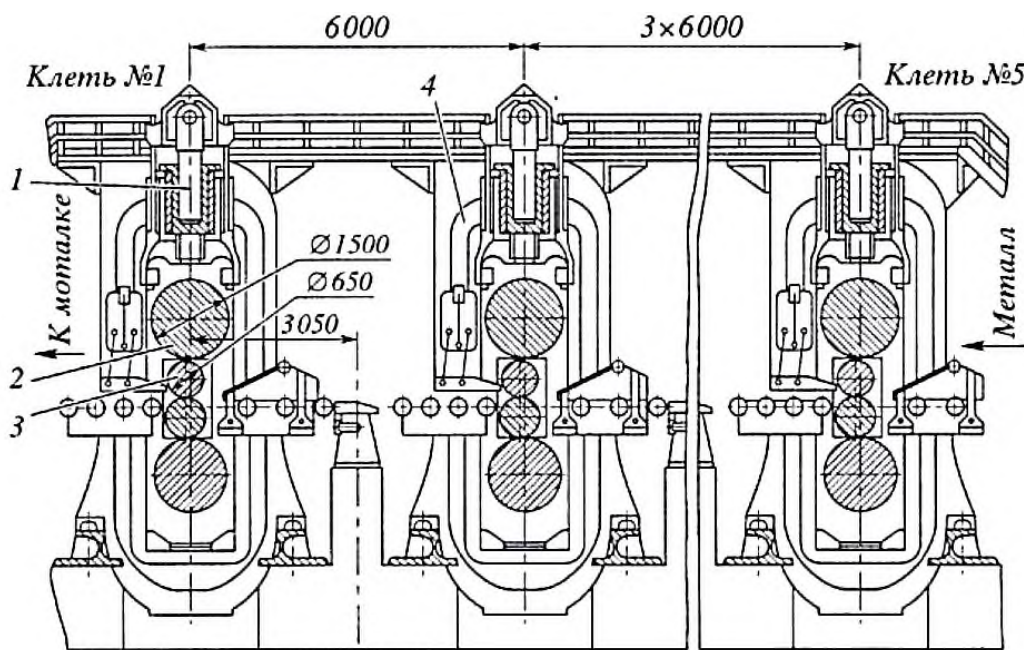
Непрерывная чистовая группа клетей 650/1500x2800 полунепрерывного стана 2800 [9]
